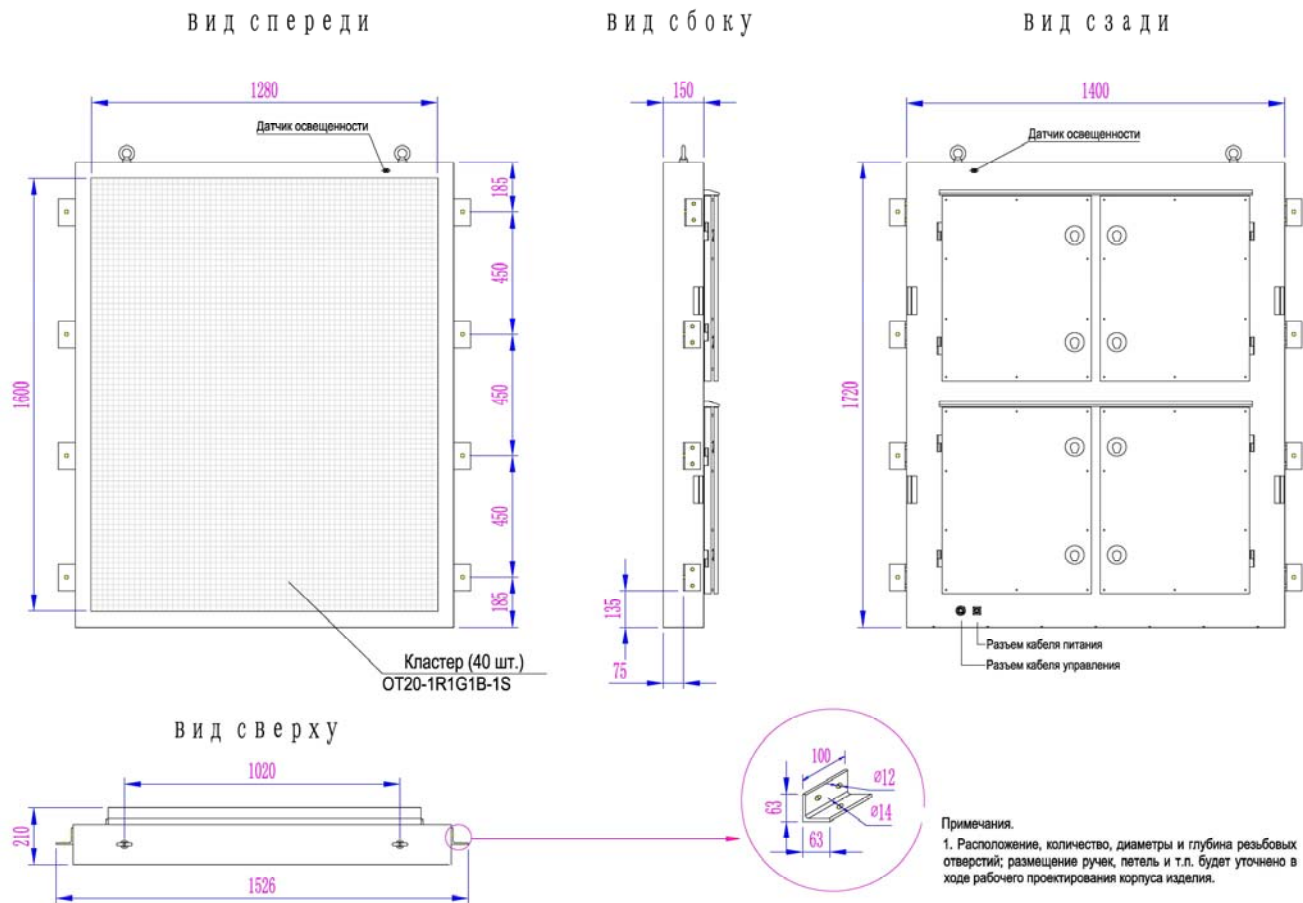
Внешний вид и основные размеры ЗПИ SMP 20C-128160.
